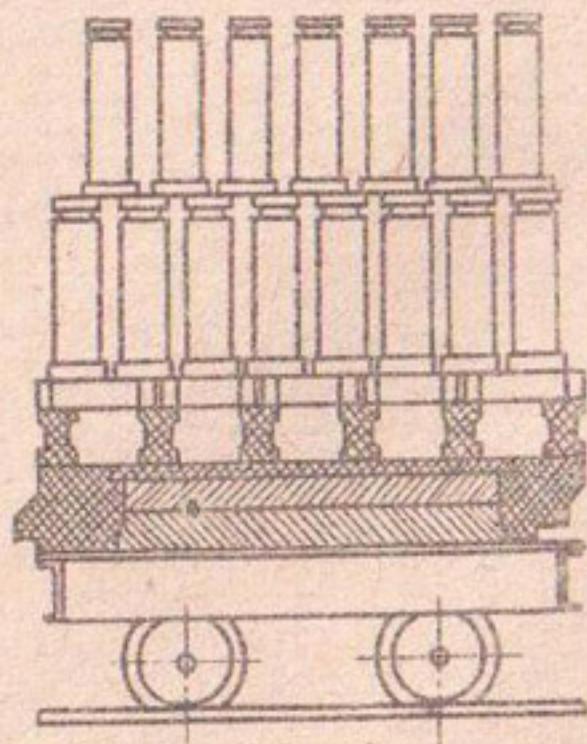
Схема садки труб на вагонетку туннельной печи для обжига.
